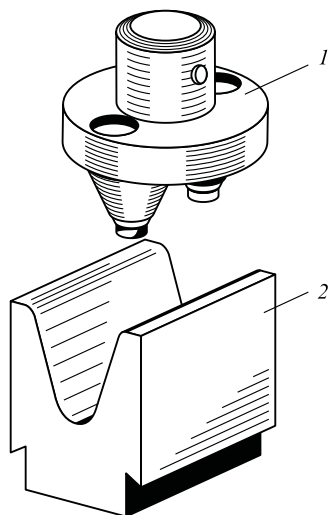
Универсальный ступенчатый аппарат для опрессовки (УСА):
